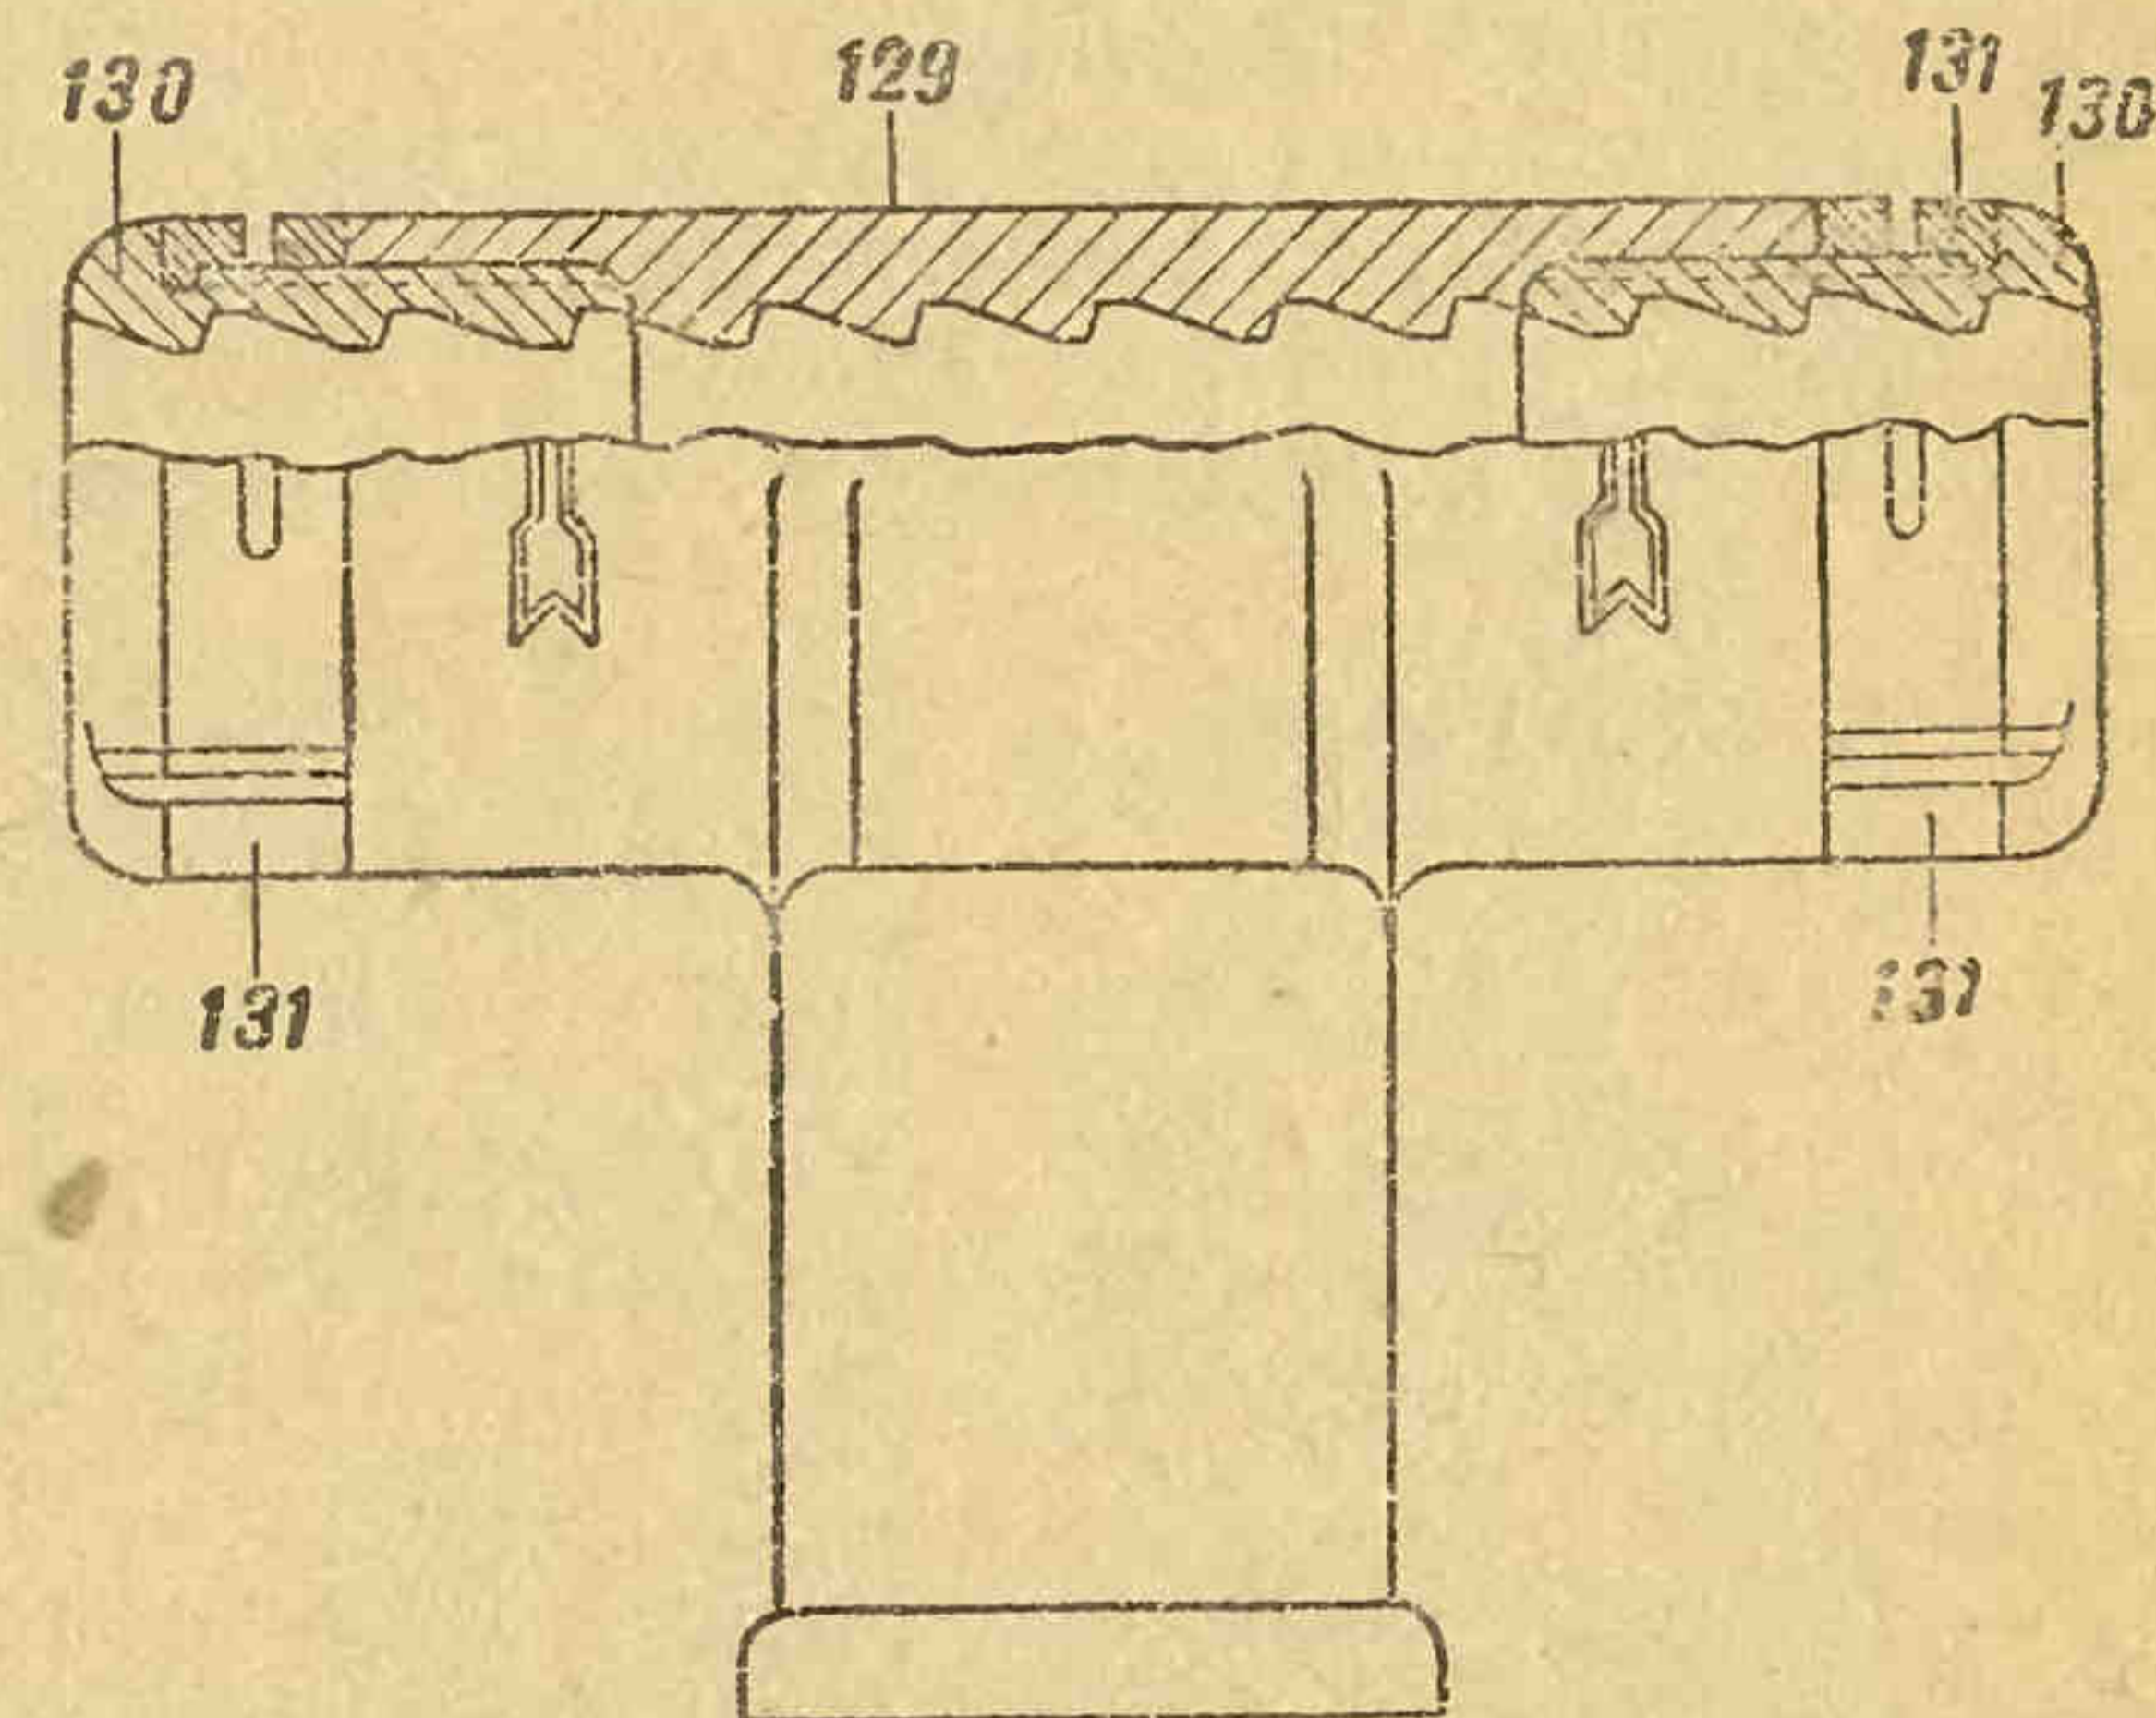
Матка поворотного механизма (сб. 3-12): *129* — корпус матки (3-56); *130* — регулирующие (втулка) гайка (3-57); *131* — контргайки (3-58).
